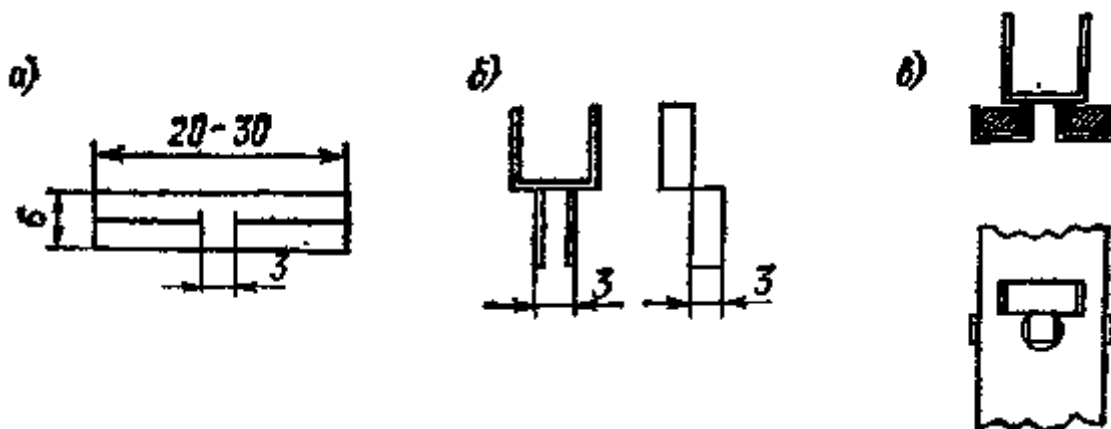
Монтажная планка: а — развертка; б — лепесток; в — установка лепестка на планку
